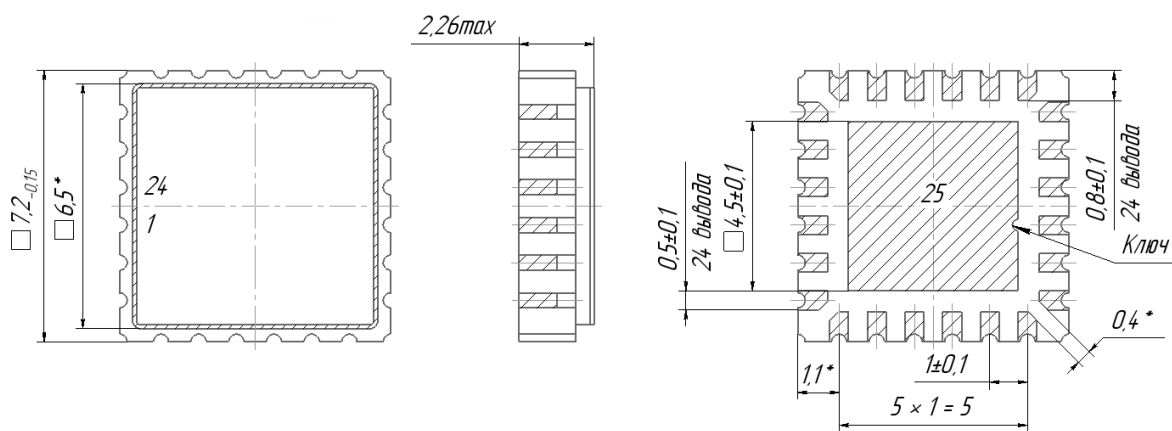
Внешний вид корпуса 5159.24-1H3
